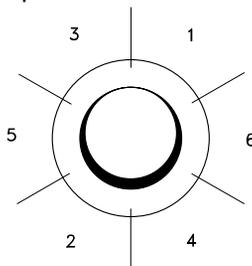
Порядок приварки адаптера к трубе / емкости
